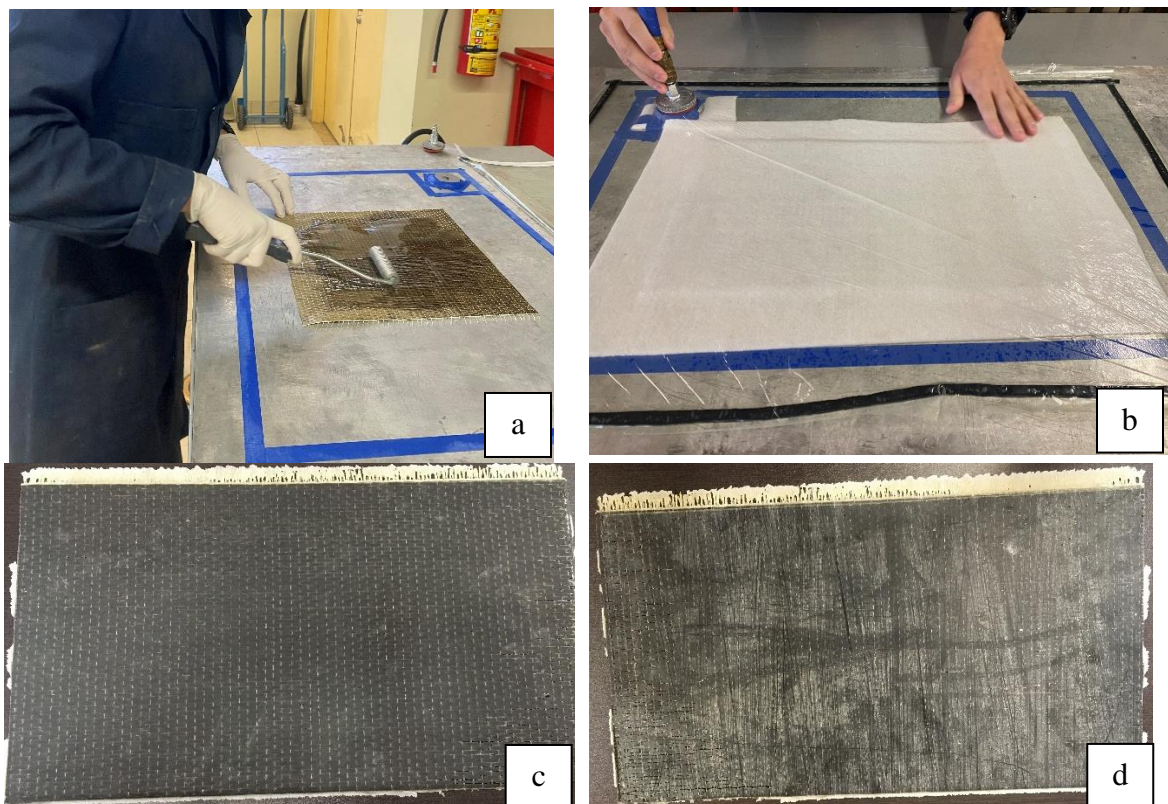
a) Proceso de laminado; b) Bolsa de vacío; c) Cara frontal del laminado; d) Cara trasera del laminado.
